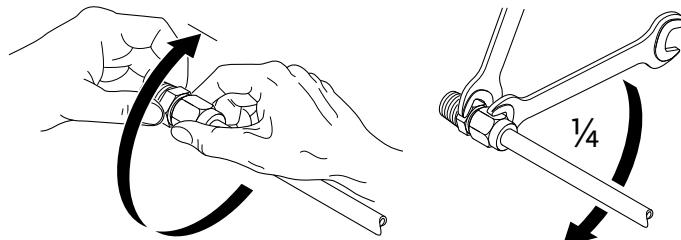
Повертання затискового різьбового кільця ще на 1/4 оберту
